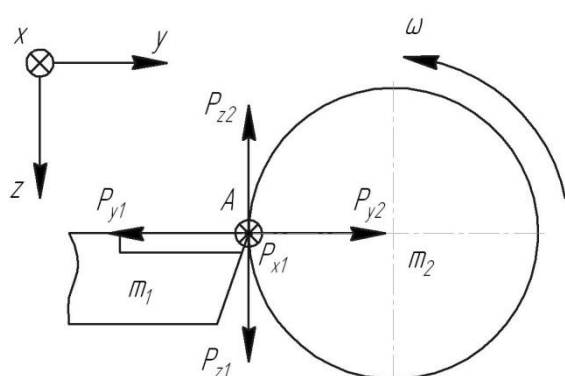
Схема сил при токарной обработке внешней цилиндрической поверхности
